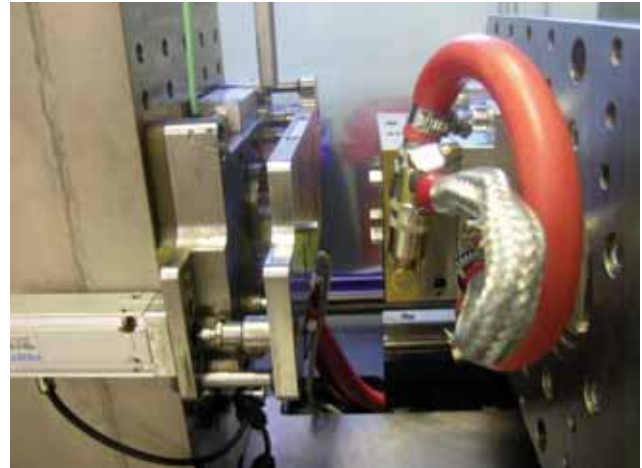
Spritzgießwerkzeug in der Spritzgießmaschine
